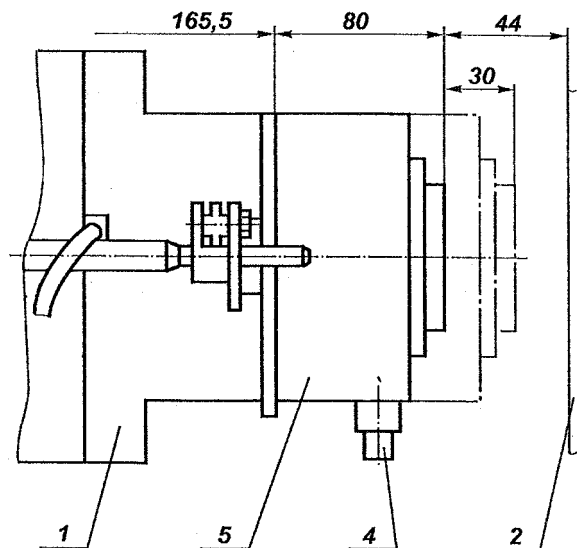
Скоба для крепления выключателей на рейках с закрытым пазом.
